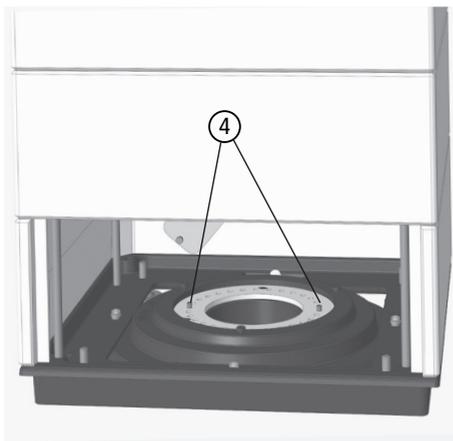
Tiges de butée, réglage des butées gauche et droite
